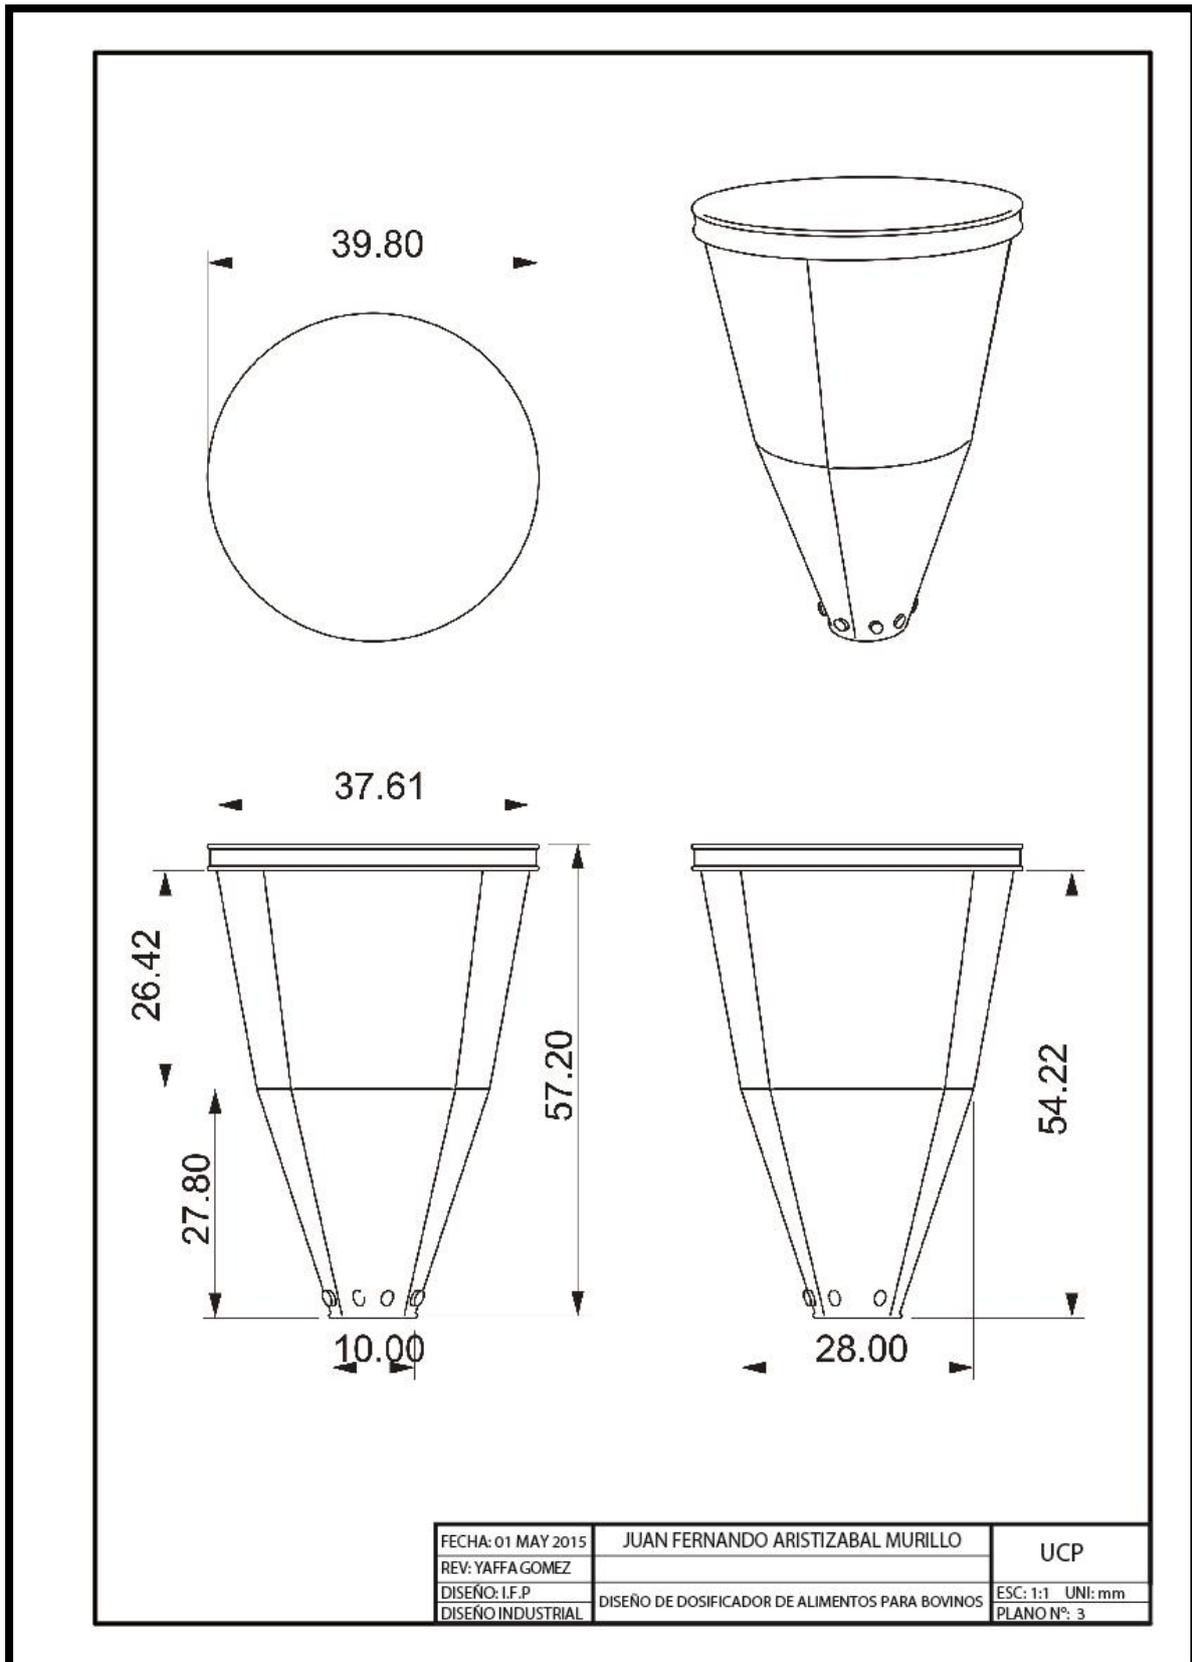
Plano contenedor. Fuente: elaboración propia
